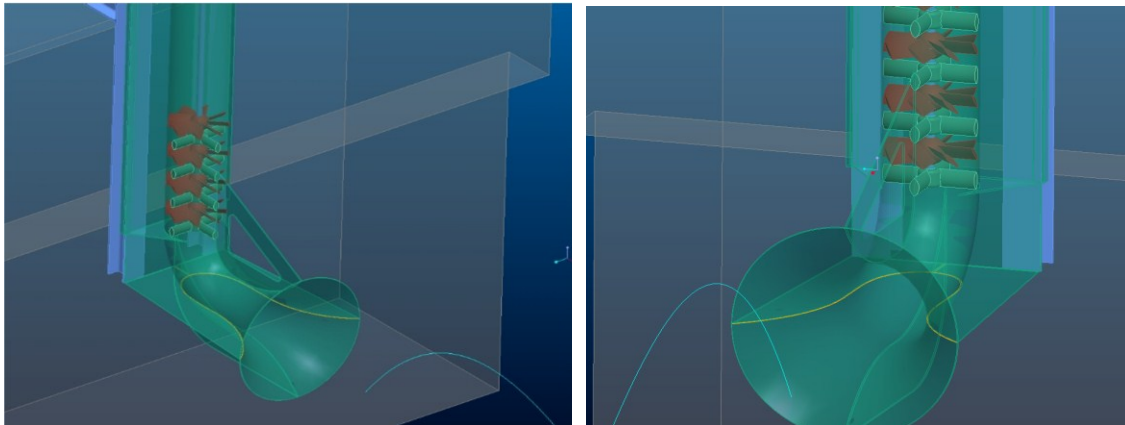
Disegno preliminare e dettagli della sezione delle eliche del Wave-Sax
